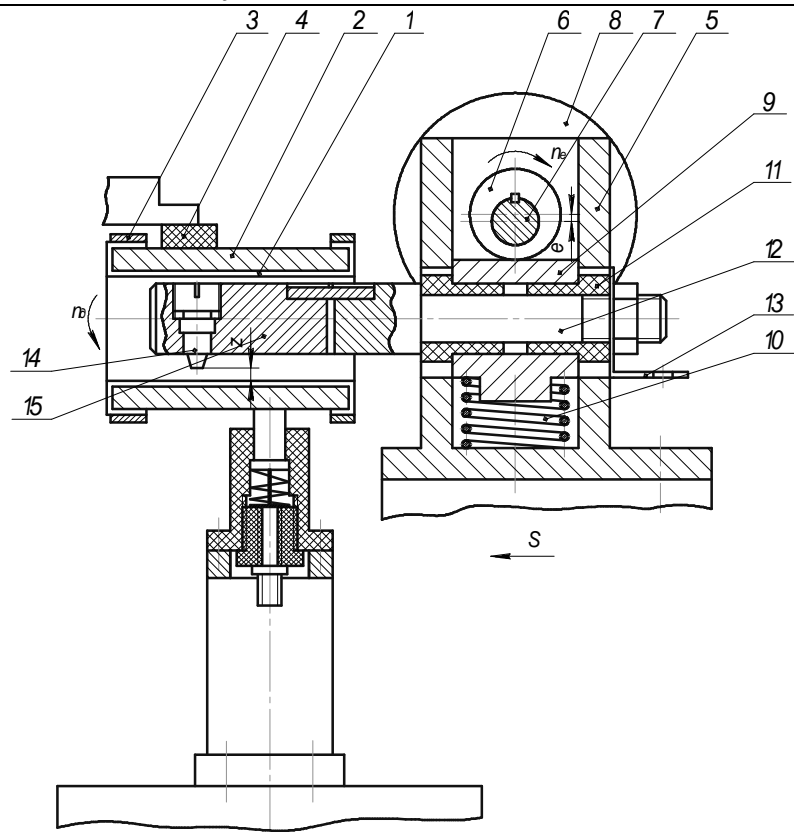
Установка деталі і пристрій з пружною штангою для електроконтактної дискретної цементації внутрішньої поверхні
